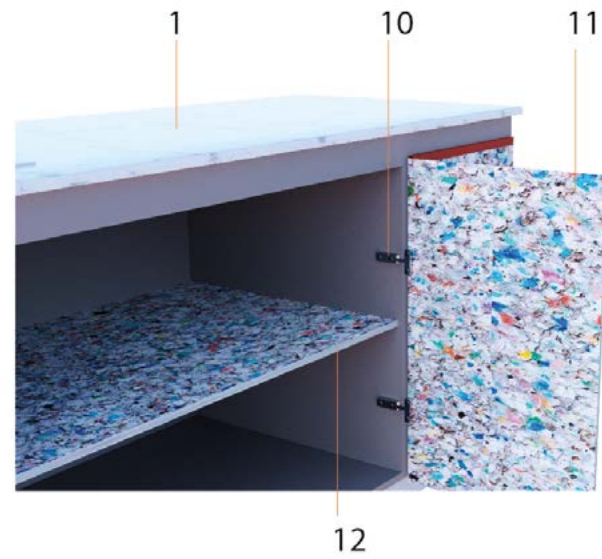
Detalle constructivo 3d mueble de cocina HDPE reciclado
